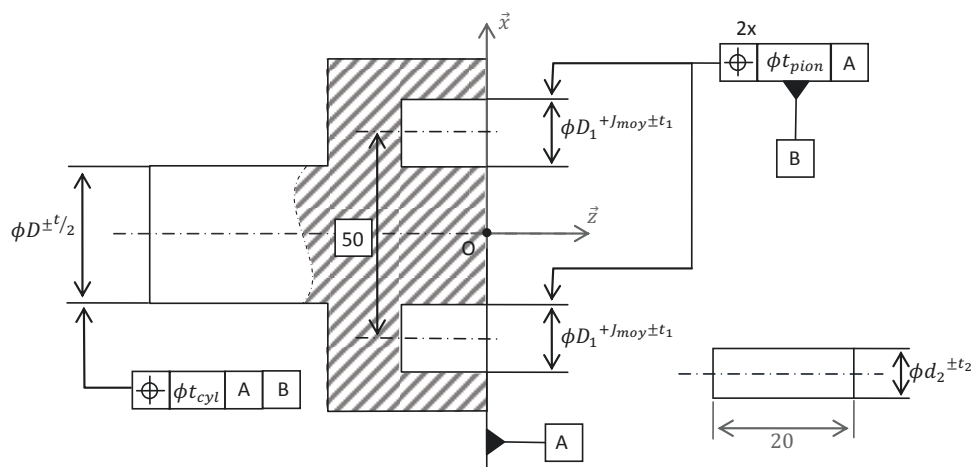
Tolérancement des pièces de l'assemblage par double piétage
